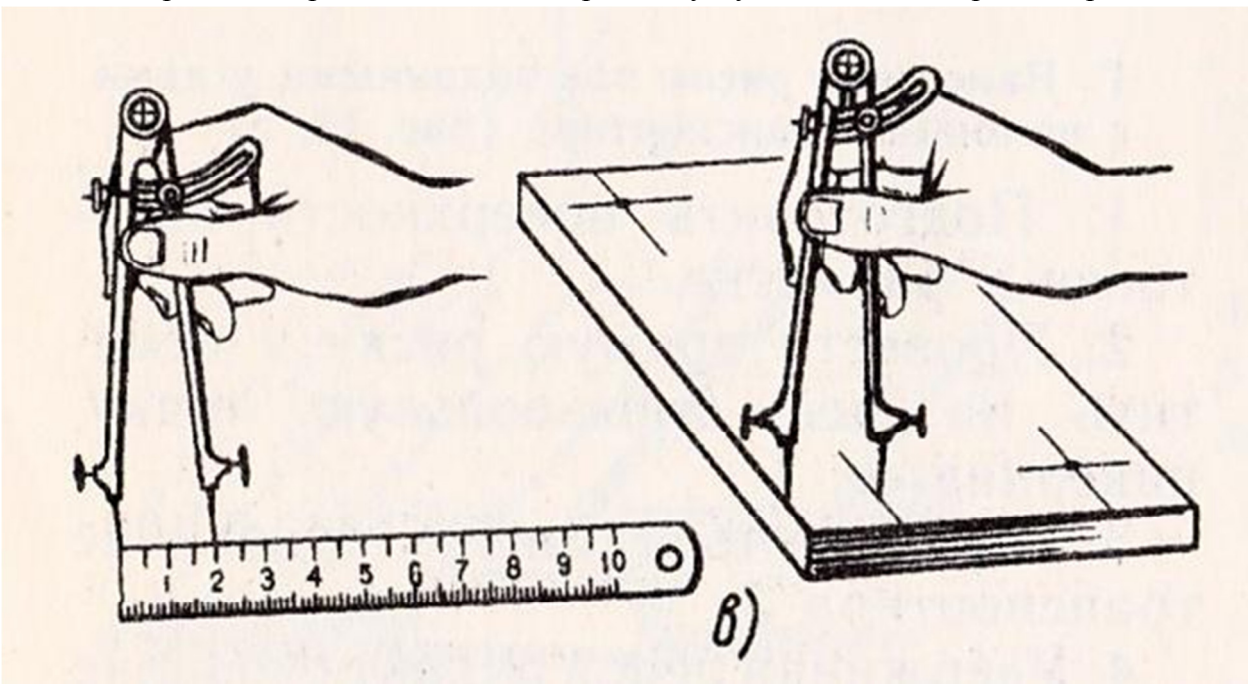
Разметка центров отверстий на данном расстоянии от ребер заготовки
